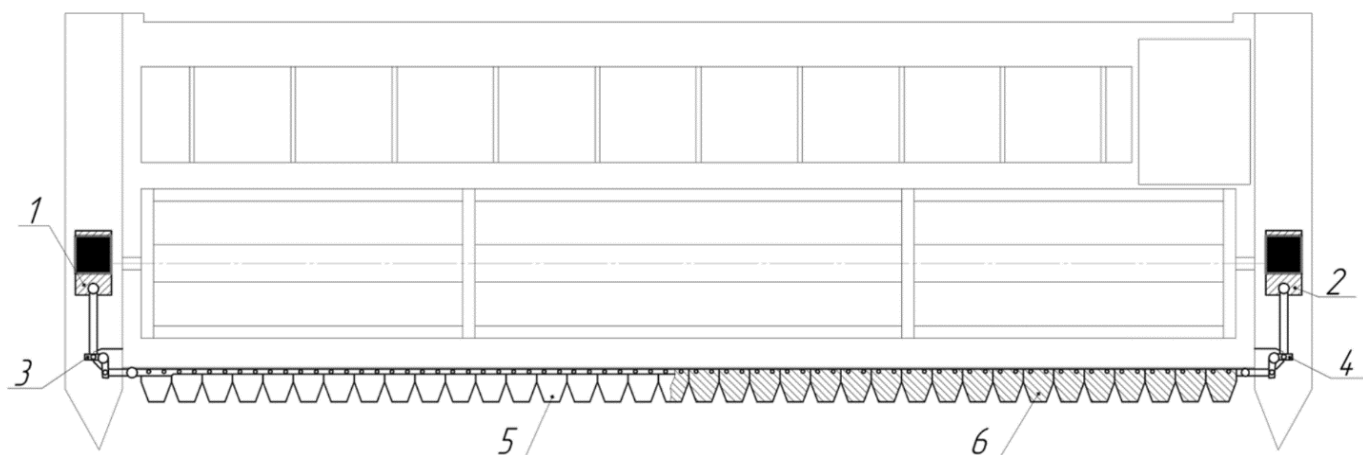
Жатка з боковим розташуванням приводних ДПЛАД: 1 – ДПЛАД приводу верхньої ножової смуги; 2 – ДПЛАД приводу нижньої ножової смуги; 3 – коромисло приводу верхньої ножової смуги РА; 4 – коромисло приводу нижньої ножової смуги РА; 5 – верхня ножова смуга РА; 6 – нижня ножова смуга РА.
